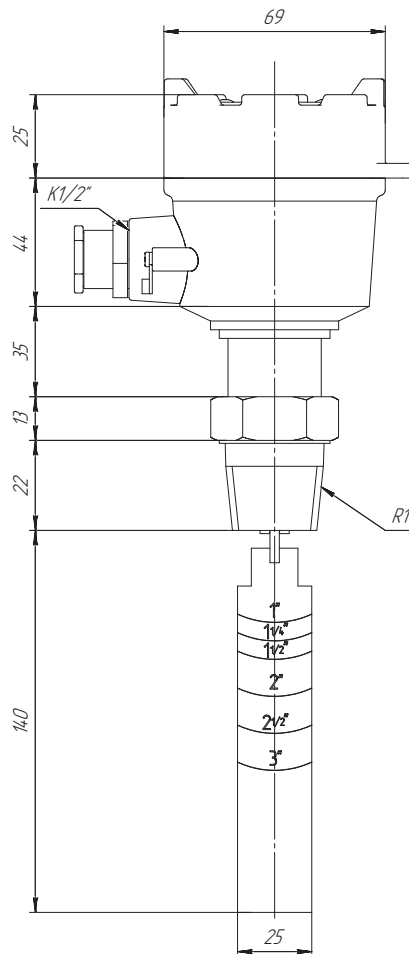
Габаритные и присоединительные размеры исполнения «Вн»
